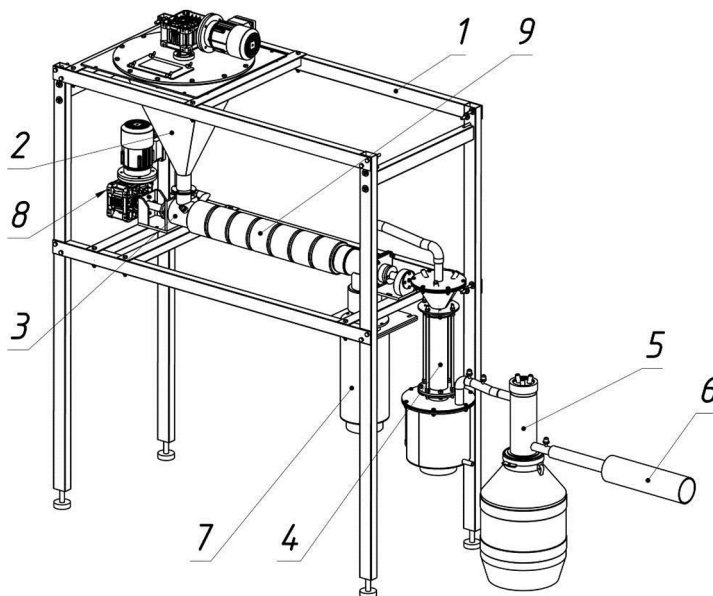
Схема установки: 1 – опорный каркас; 2 – дозатор; 3 – шнековый реактор; 4 – конденсатор № 1; 5 – конденсатор № 2; 6 – отвод газа; 7 – бак углерода; 8 – мотор-редуктор; 9 – электрические нагреватели
